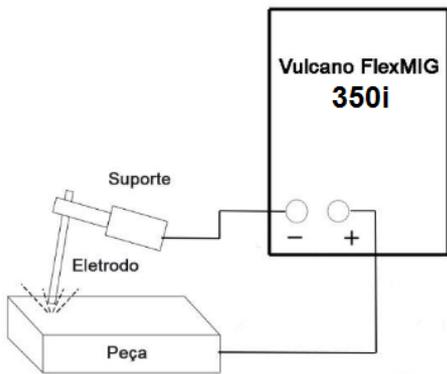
Conexão positiva para soldagem com eletrodo revestido
